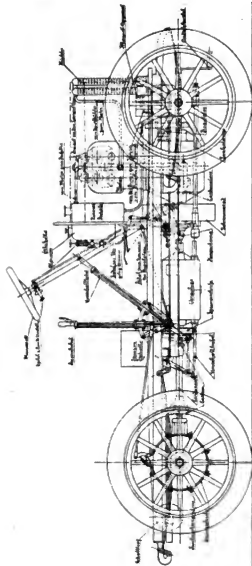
und 7. Aufsicht und Grundriss des Parsifal-Wagens.
